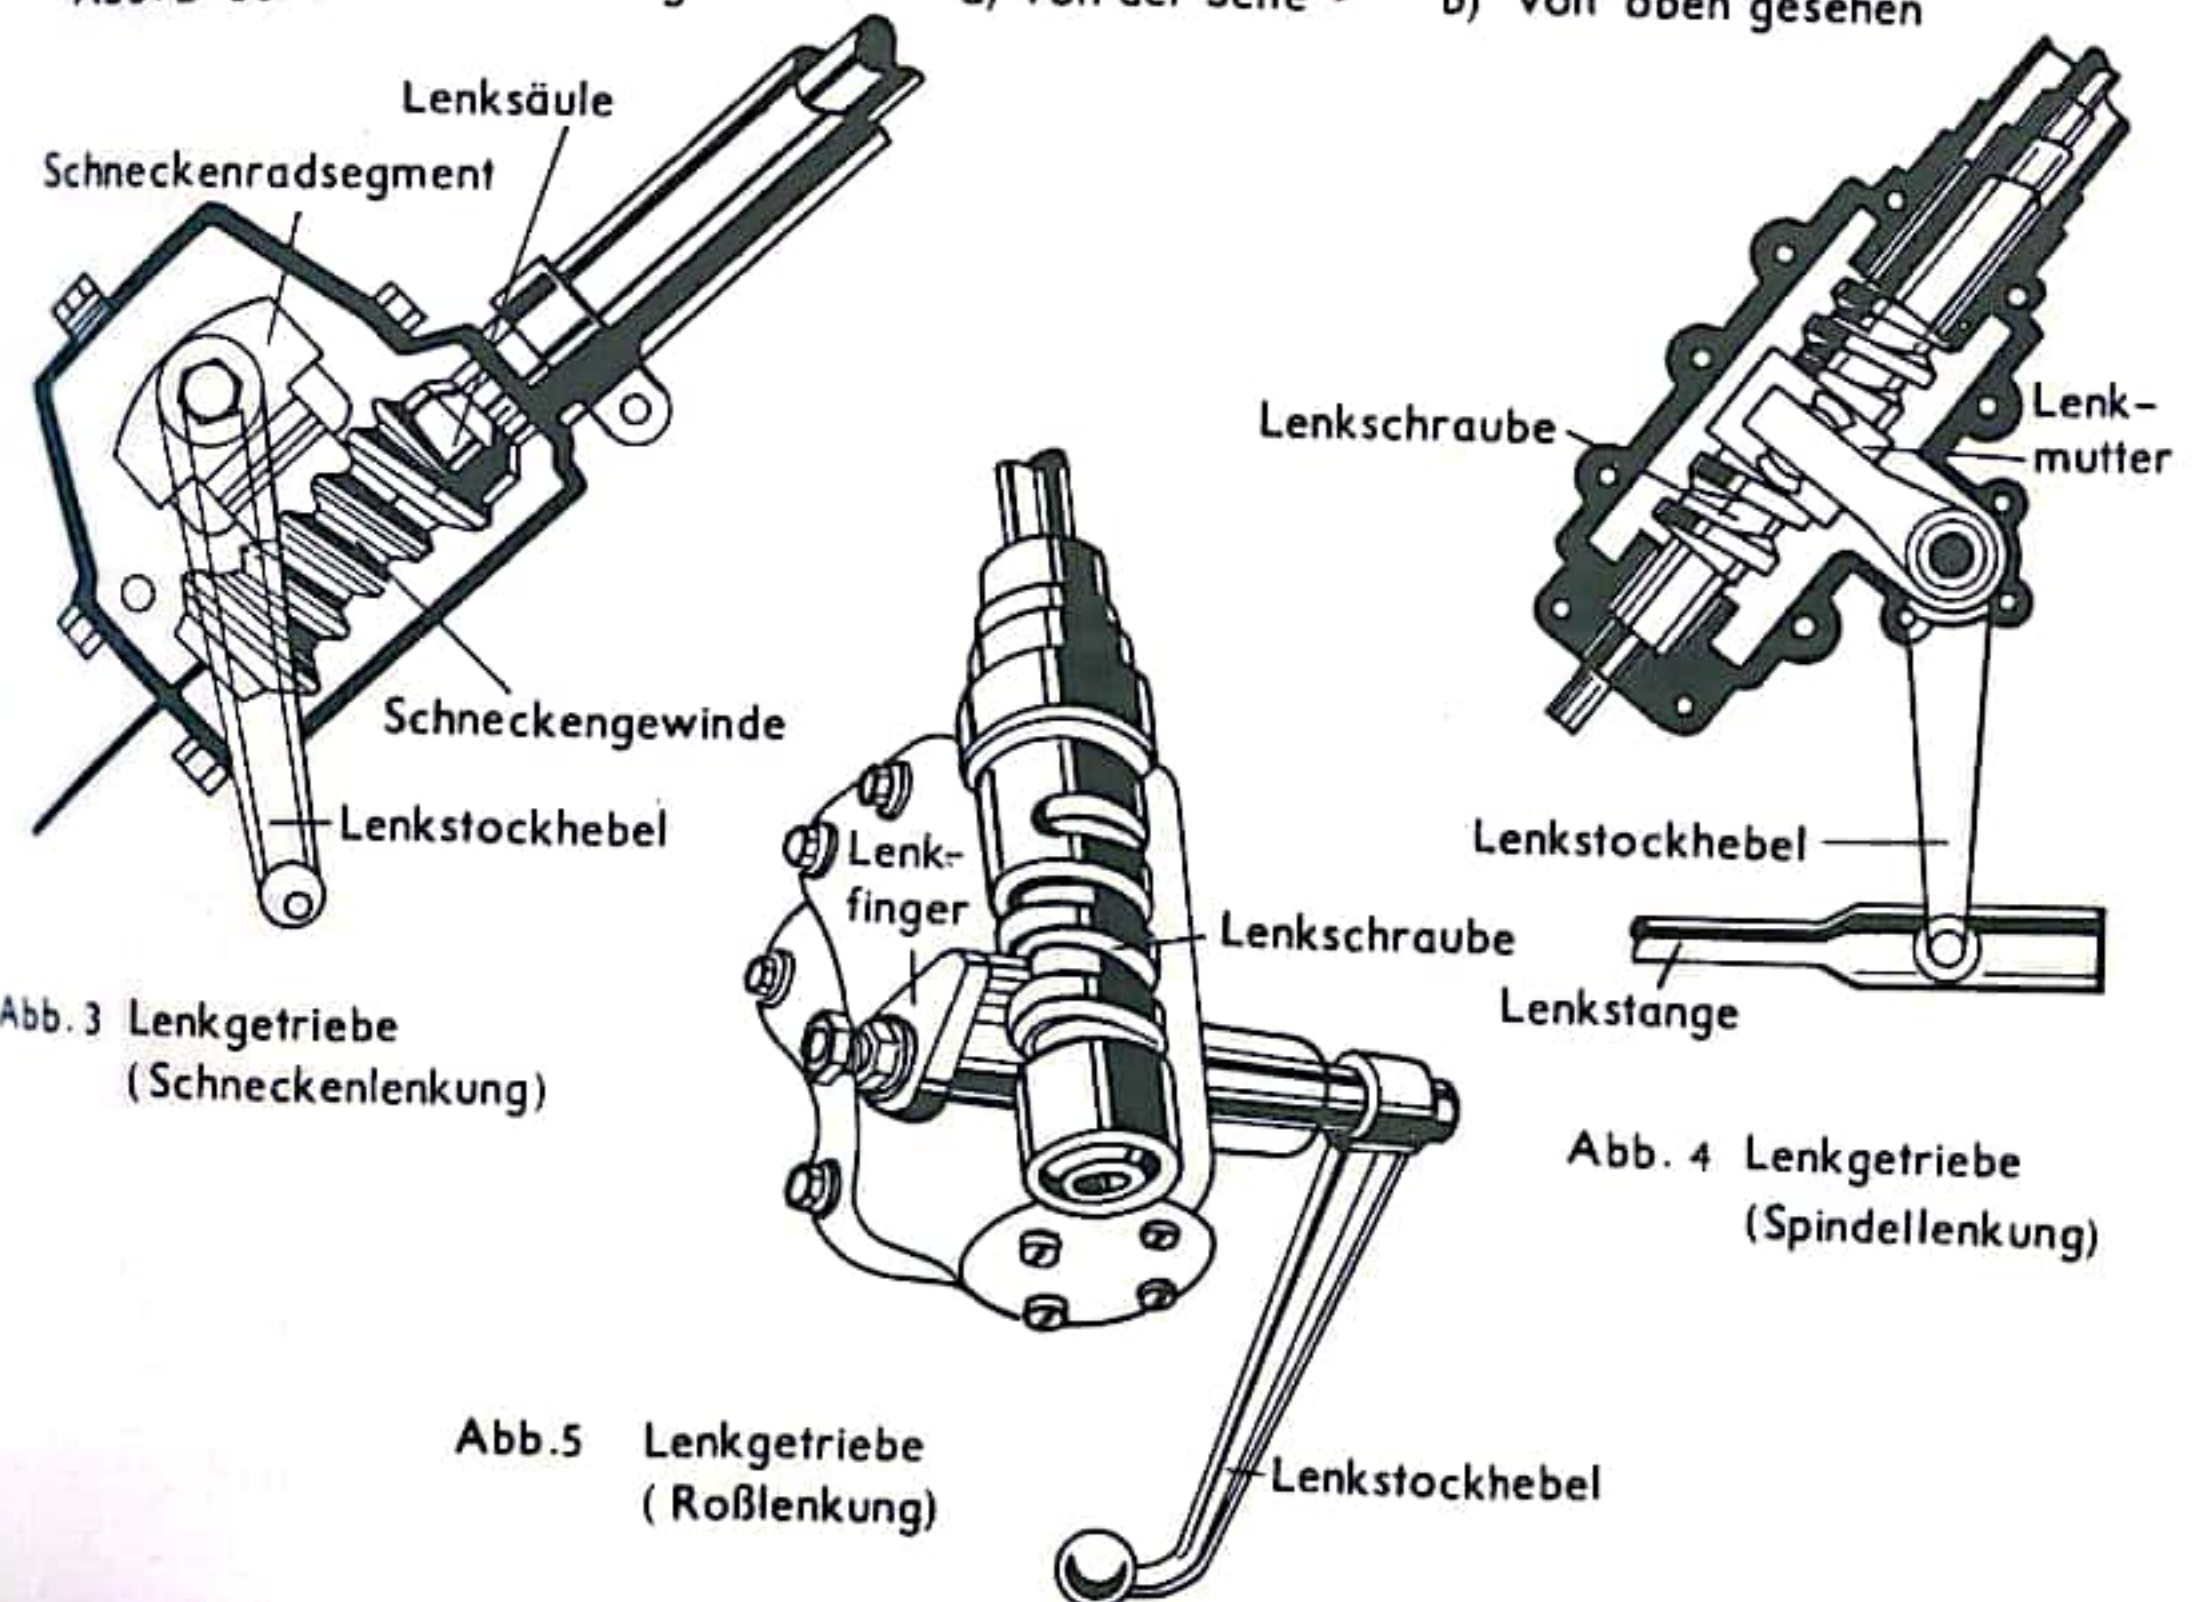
Lenkgetriebe (Schneckenlenkung)
